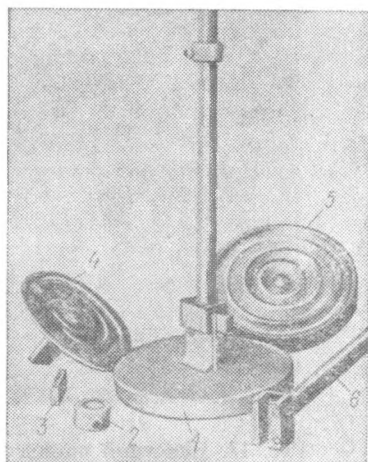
Литой анод и устройство для его крепления в заливном колоколе:
